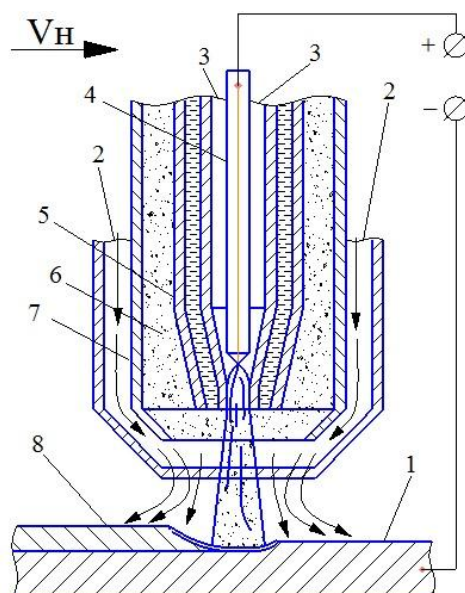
Схема процесса плазменной наплавки с вдуванием порошка в дугу
